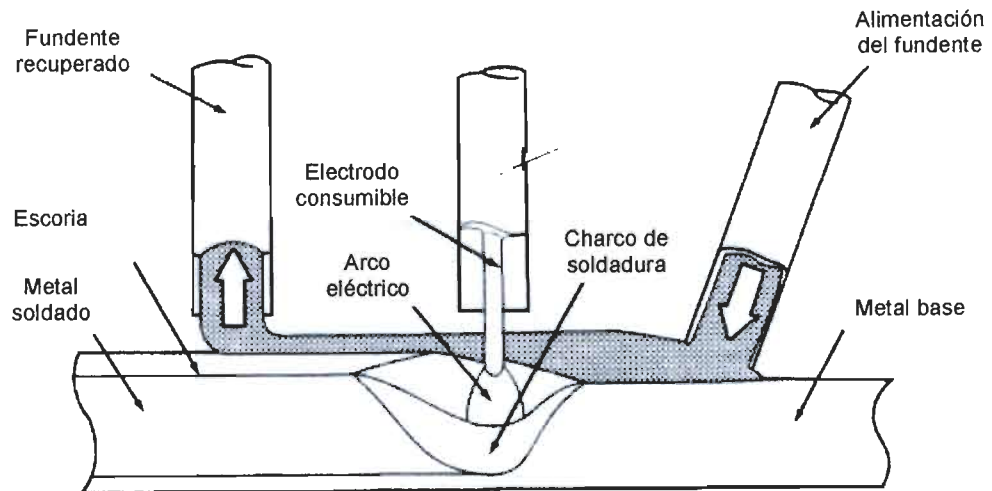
Proceso de soldadura por arco sumergido SAW⁽⁶⁾.
